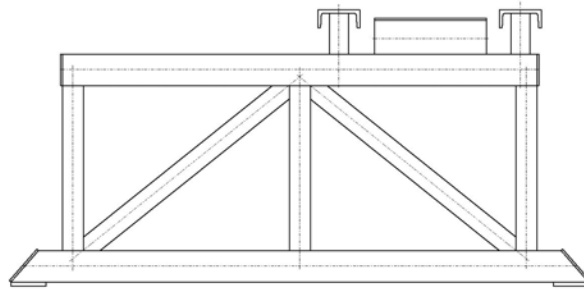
Vista frontal de la estructura tipo armadura de la máquina.
